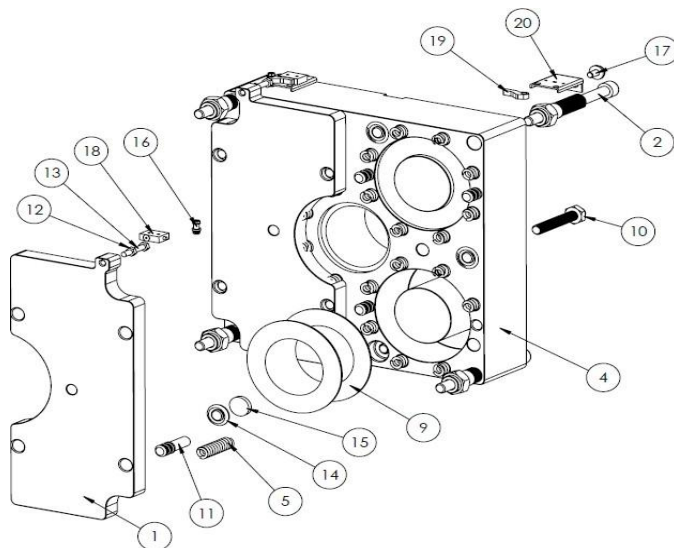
Vista en despiece del conjunto de bobinas de freno Aemf I-2-8
